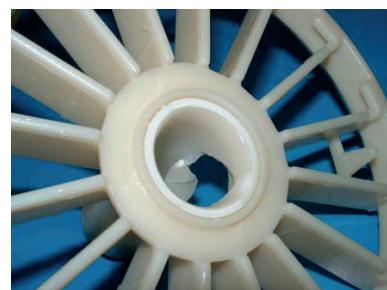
Rotta del tubo permeato nell' area adiacente alla connessione col tappo/ High-pressure failure of product water tube in area adjacent to weld with endcap.
